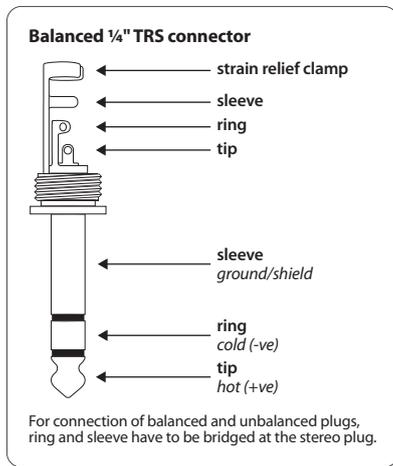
Connecteur jack stéréo 6,3 mm
